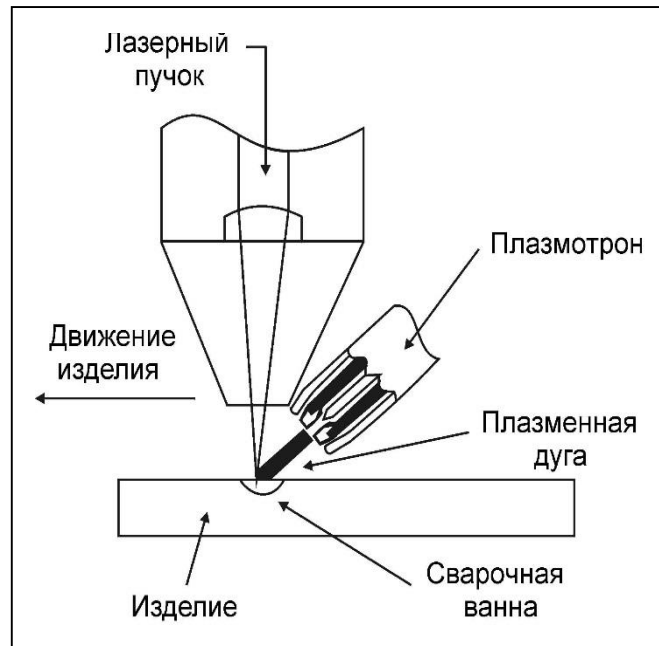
Схема процесса лазерно-плазменной сварки [12].
